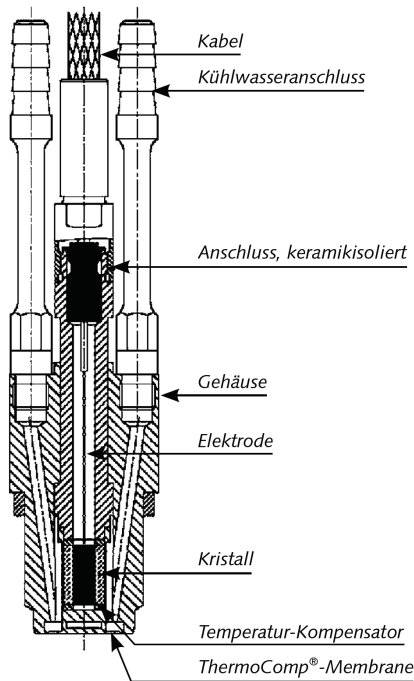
Wassergekühlter Zylinderdrucksensor (Schnittansicht) [41]
